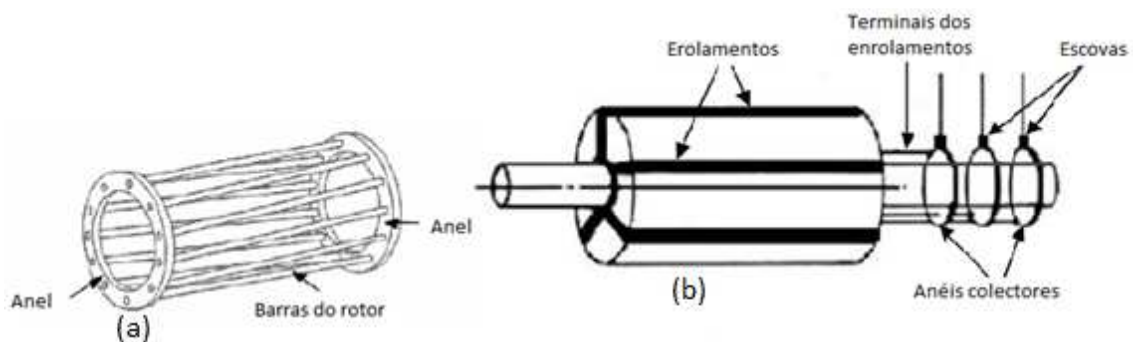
Esquema do rotor em gaiola de esquilo (a) e bobinado (b)
